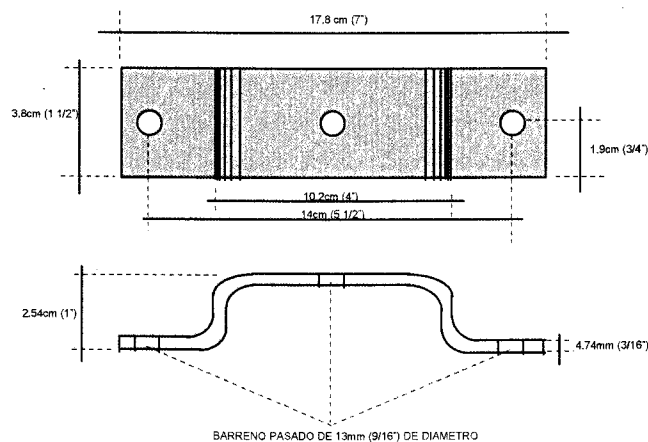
FIGURA TORNILLERÍA PARA FIJAR A MUROS Y ESTRUCTURAS METÁLICAS.
